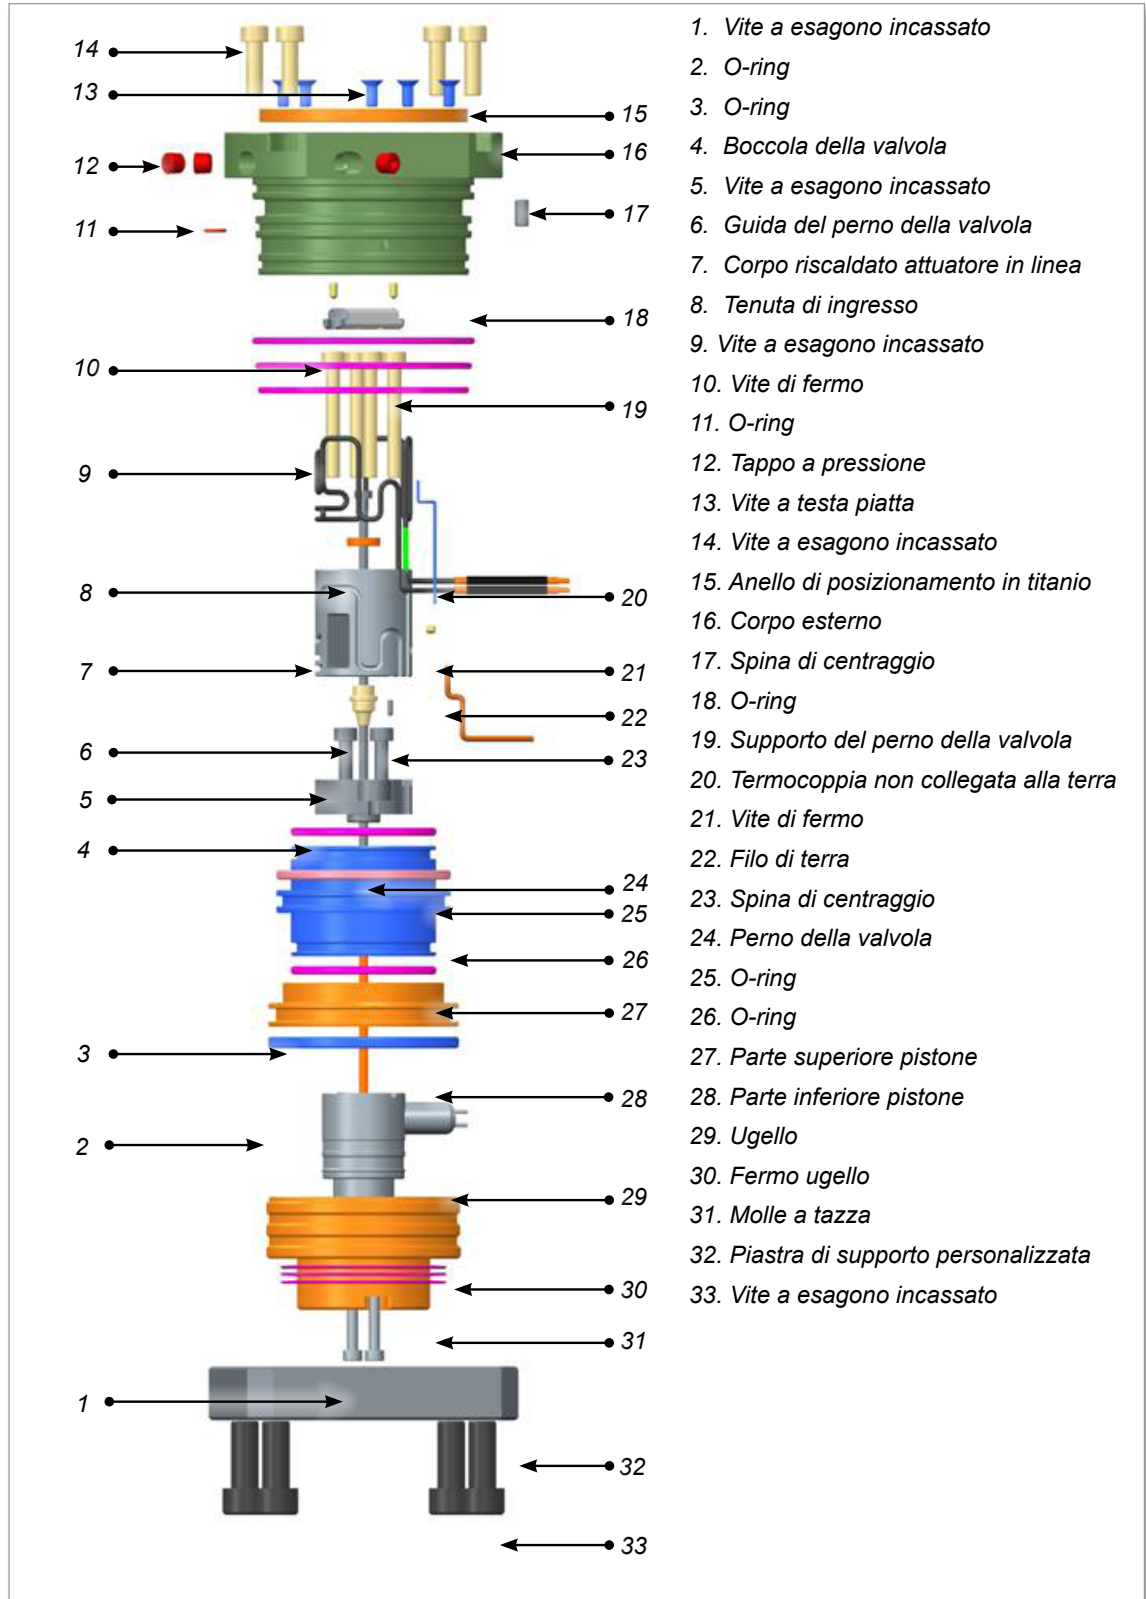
Assemblaggio dell'attuatore Slimstack
